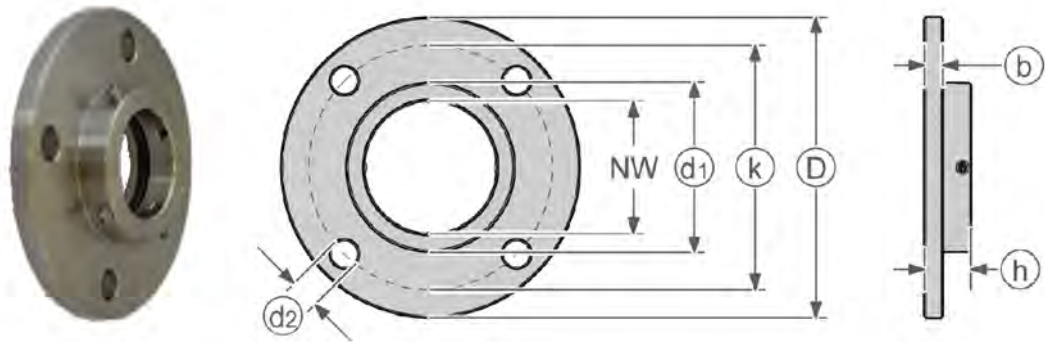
Dimensions bride coulissante brûleur d'allumage GFI
